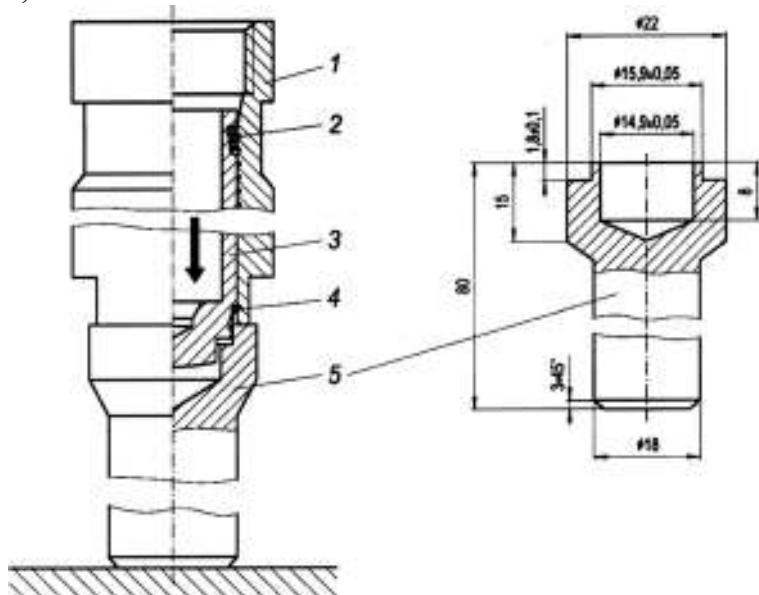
«Зарядка» гидронатяжителя с помощью оправки: 1 – корпус; 2 – запорное кольцо; 3 – плунжер; 4 – стопорное кольцо; 5 – оправка
